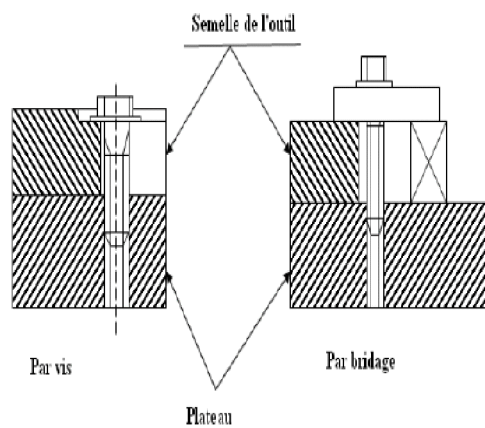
Système de fixation des semelles sur un plateau de presse.
